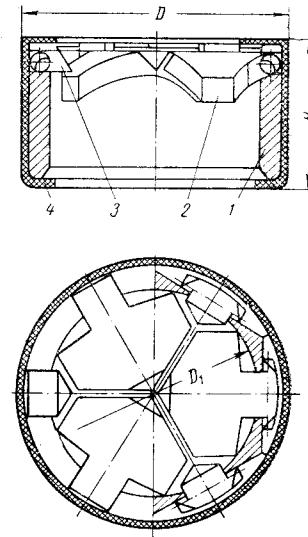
Рычажковый плавающий кернорватель Р16М.
